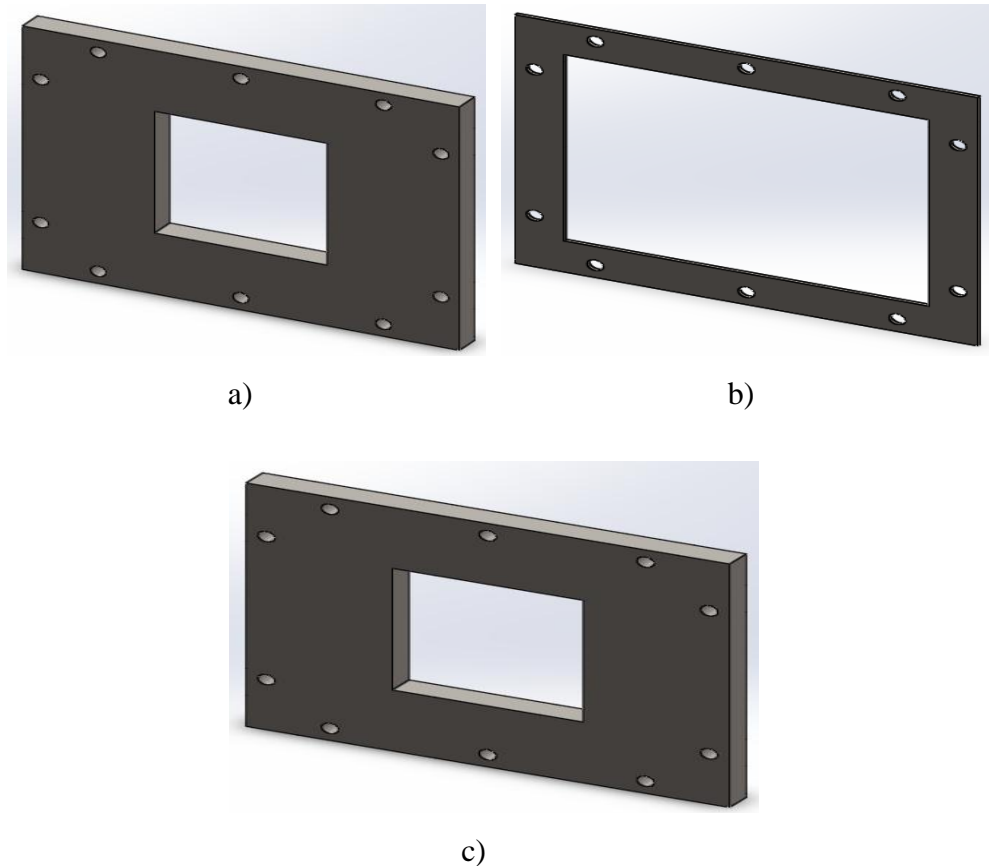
a) Marco del molde compresión b) Marco del molde Tracción c) Marco del molde Dureza
